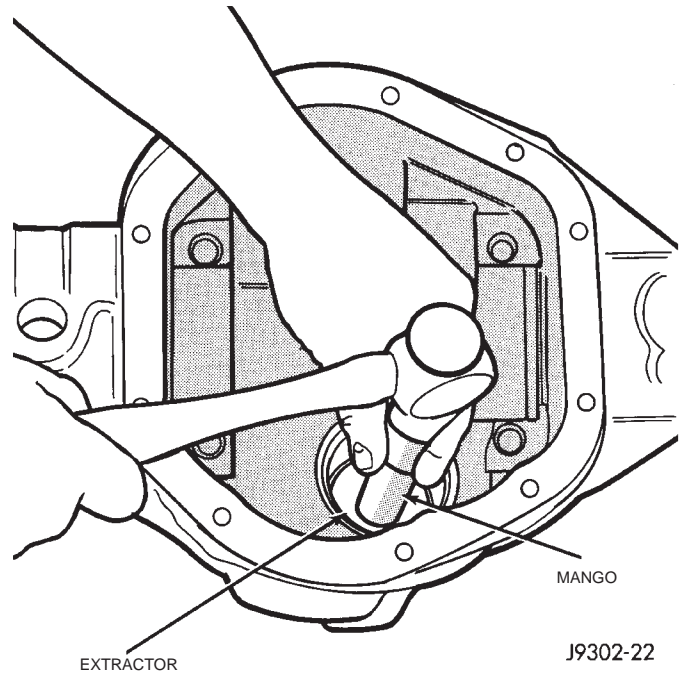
Desmontaje de la cubeta del cojinete delantero
